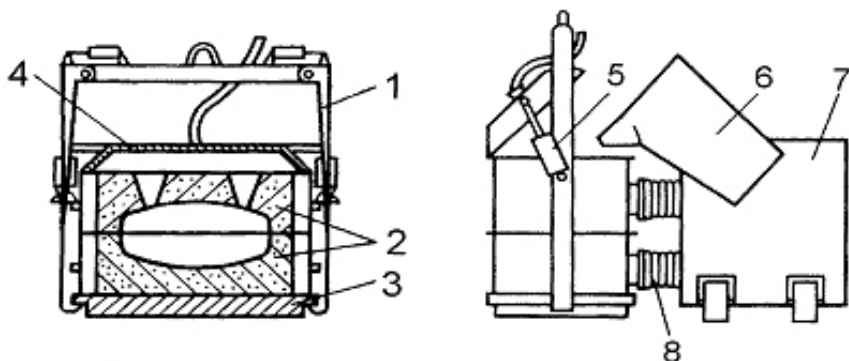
Схема устройства для создания повышенного давления на песчаную форму: 1 – элемент подвесного контейнера; 2 – полуформы; 3 – транспортная плита; 4 – герметизирующая крышка; 5 – привод; 6 – ковш; 7 – заливочная машина; 8 – клапаны
